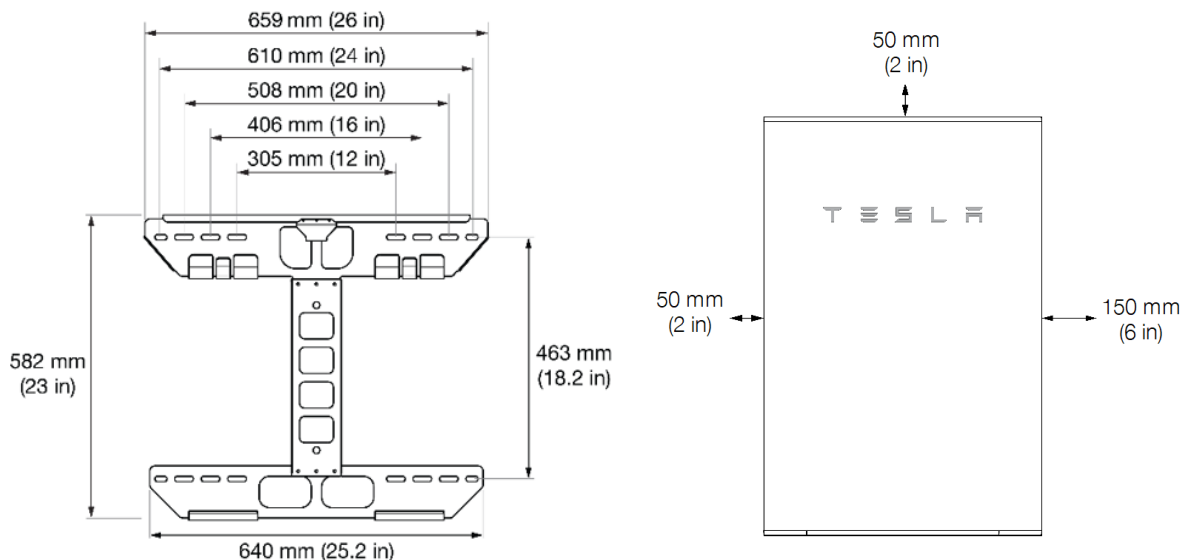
Abmessungen und Platzbedarf der Powerwall 2-Montagehalterung
